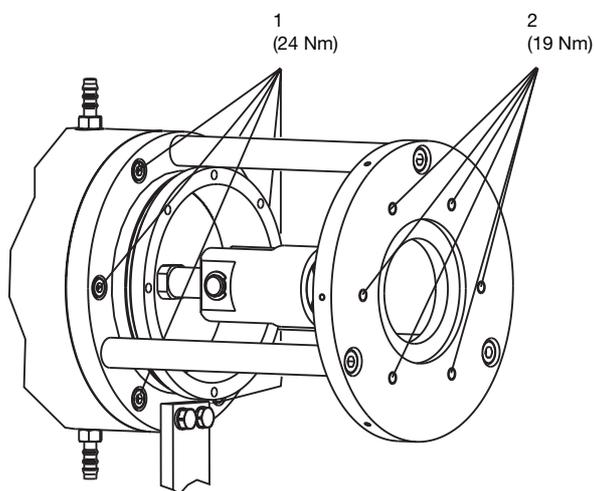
Module de dosage à piston Makro/ 5 (M5Ka)
